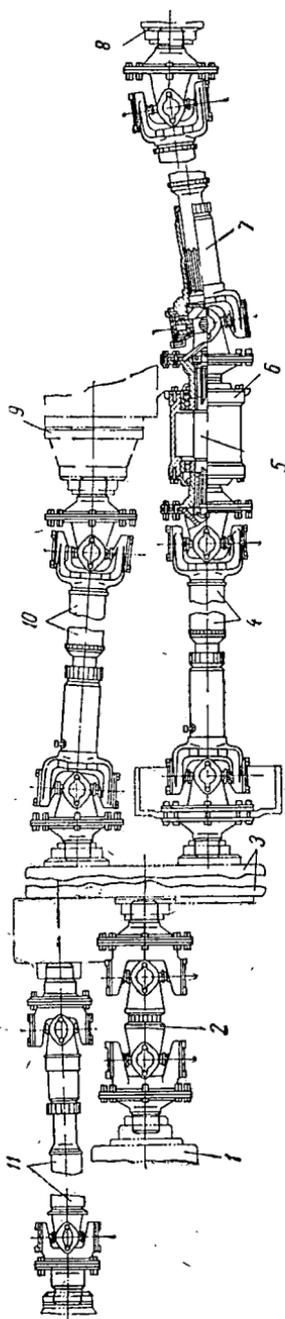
Схема передачи крутящего момента на ведущие колеса трехосного автомобиля КраЗ-214:
